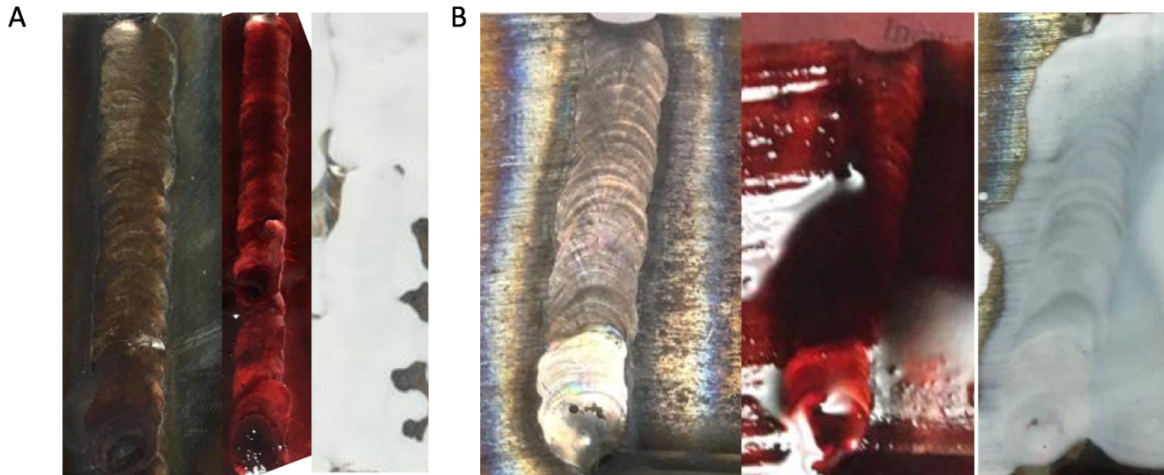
Ensayo de líquidos penetrantes a piezas soldadas. A) cordón realizado a 80 A. B) cordón realizado a 100 A.
